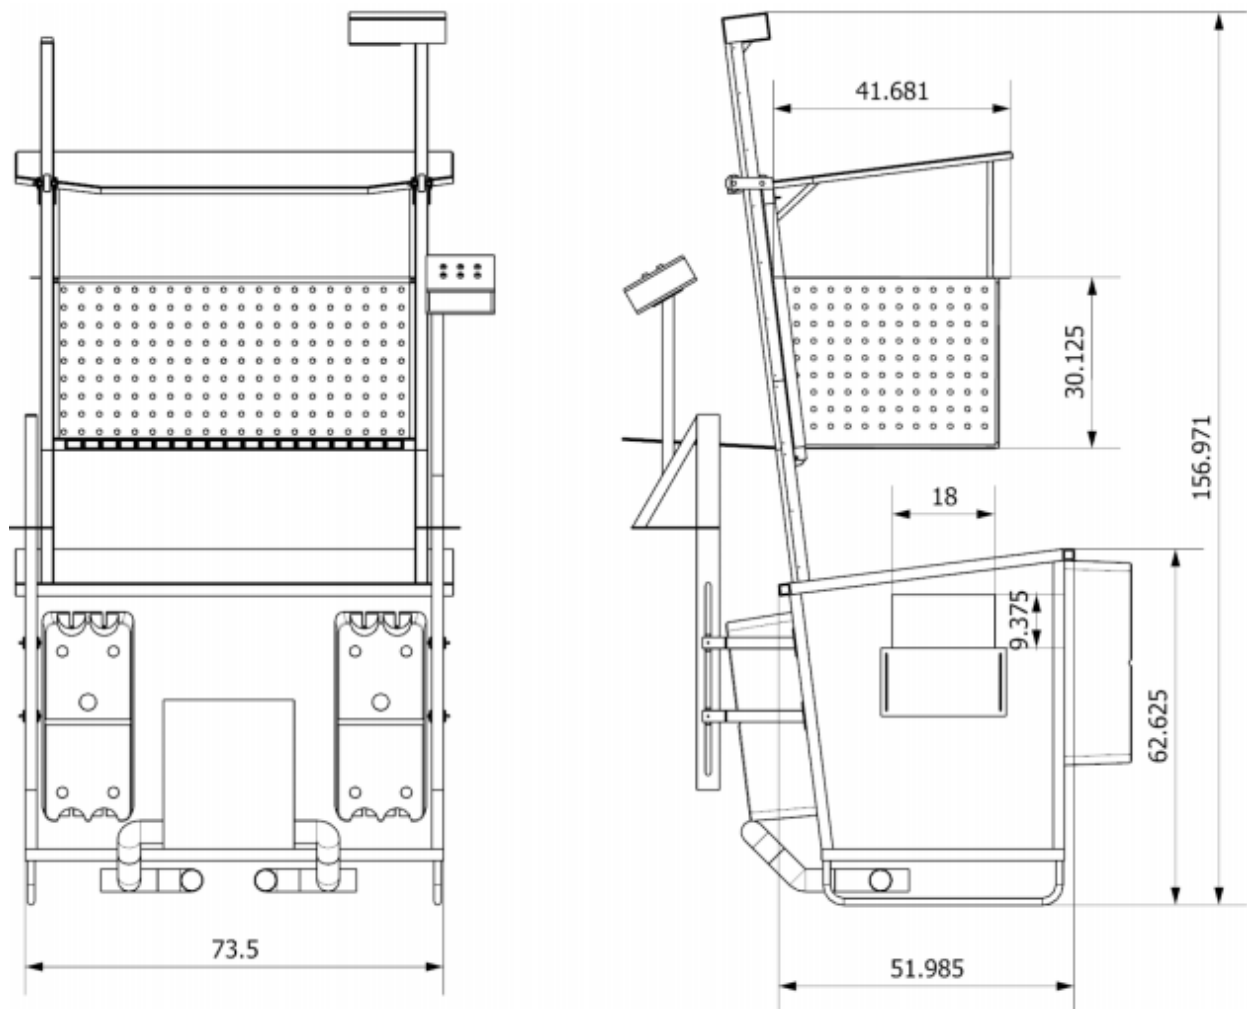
Dimensions del Harbor Skimmer (cm) (1)
